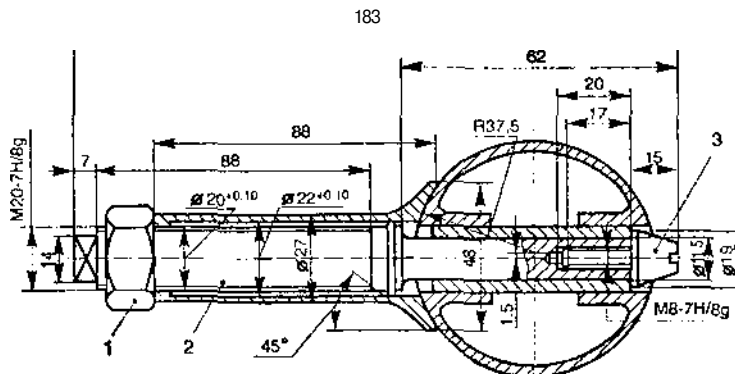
Приспособление для выпрессовки поршневого пальца: 1 - гайка; 2 - оправка; 3 - наконечник.
